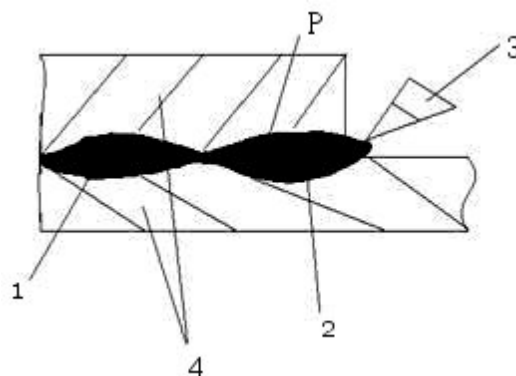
Введение клея в зазоры: 1 – сварная точка; 2 – клей; 3 – шприц; 4–свариваемые детали.
